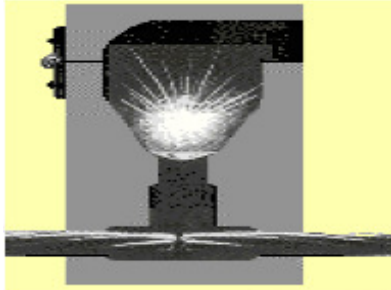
Realización de una soldadura cuproaluminotérmica.
